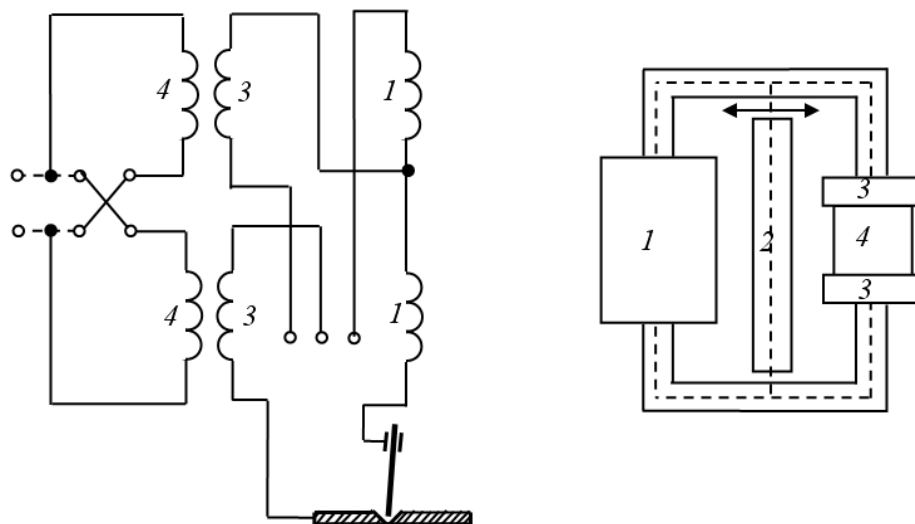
Transformateur de soudage avec un shunt magnétique mobile :
